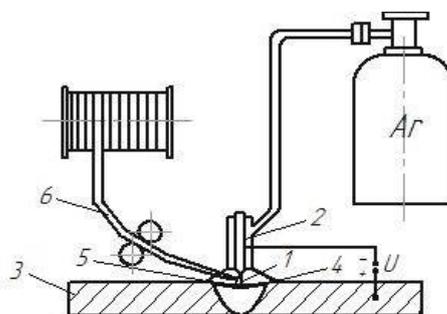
Механизированная сварка в среде защитных газов
